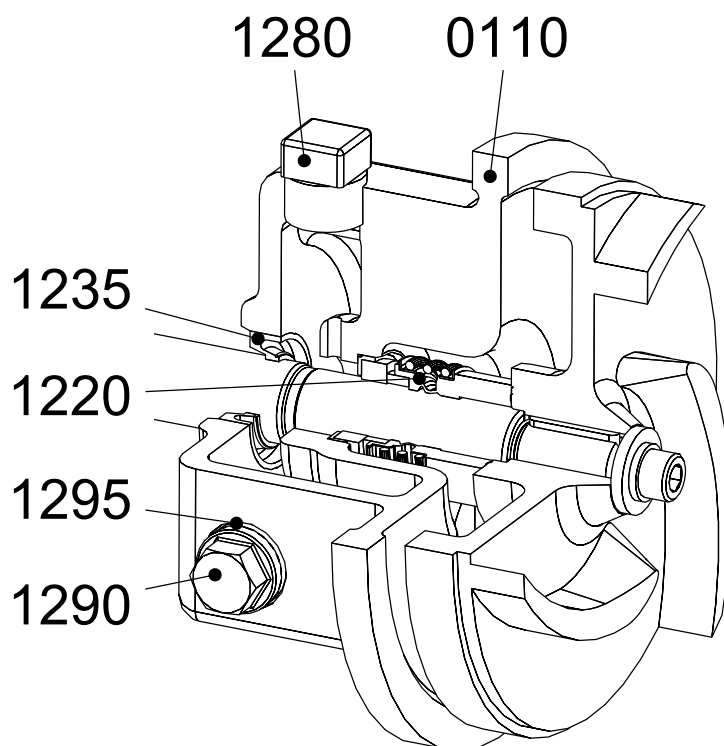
Чертеж в разрезе - Механическое уплотнение MG12.
